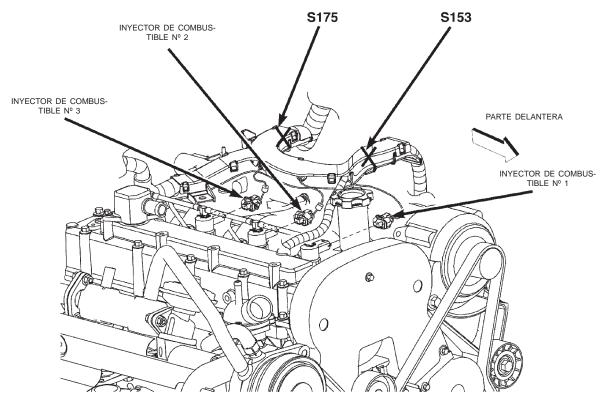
PARTE DELANTERA DEL MOTOR DIESEL
